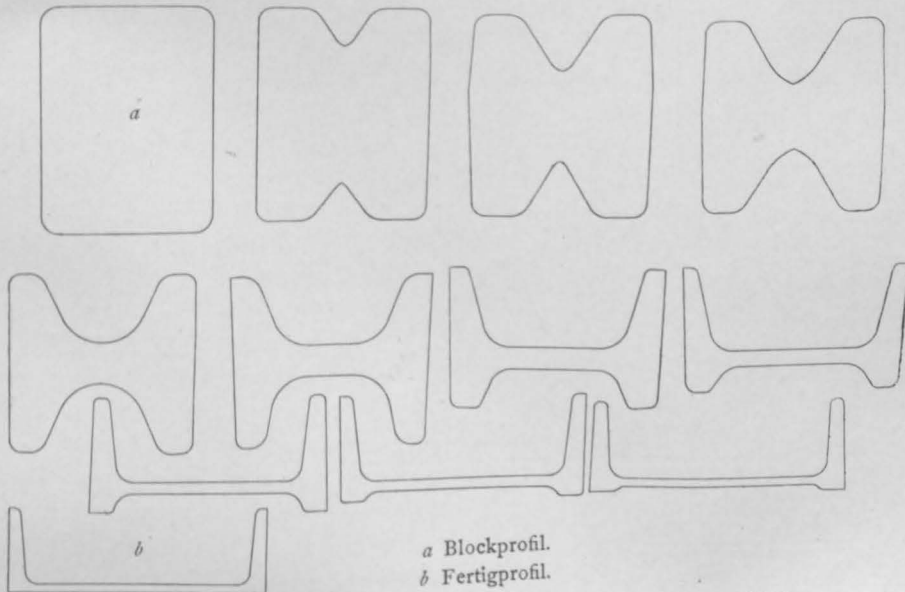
Umriss der Walzenfurchen (Kaliber) für das Walzen der U-Eisen.
